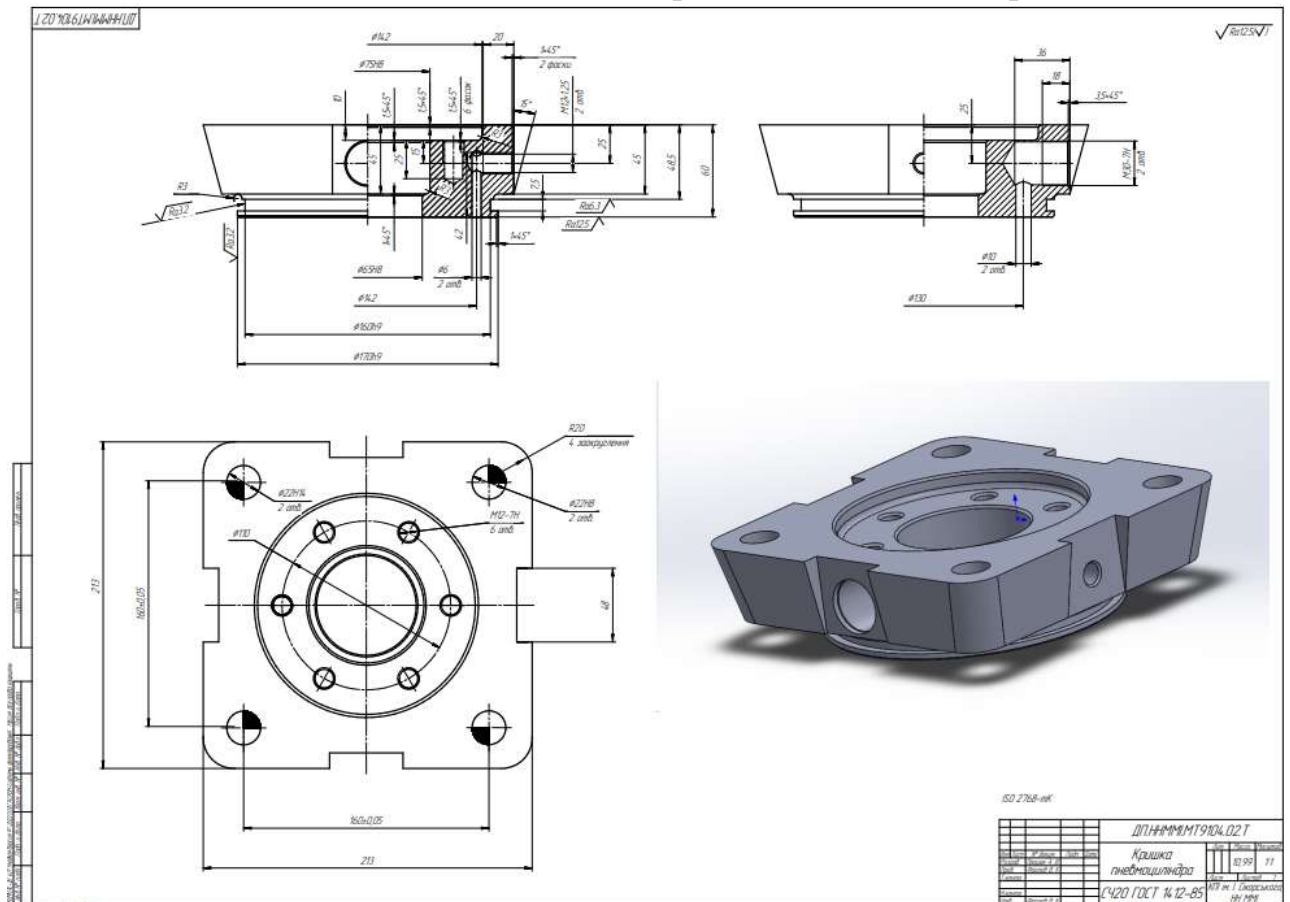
Кресленик деталі «Кришка пневмоциліндра»
